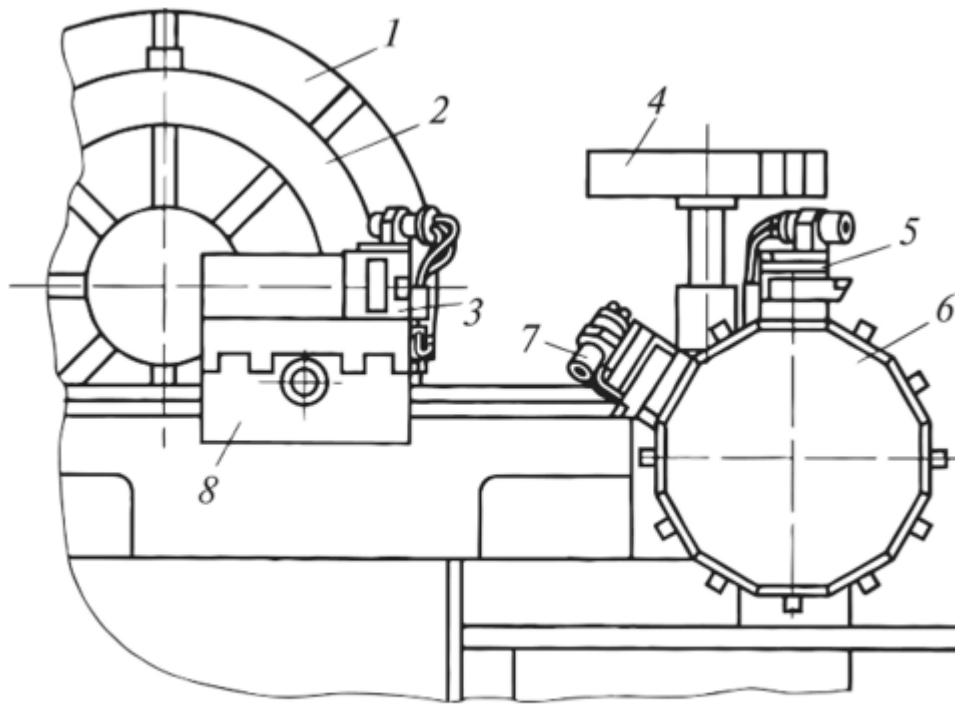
Схема установки сменного плазменно-инструментального модуля на лоботокарном станке с ЧПУ:
